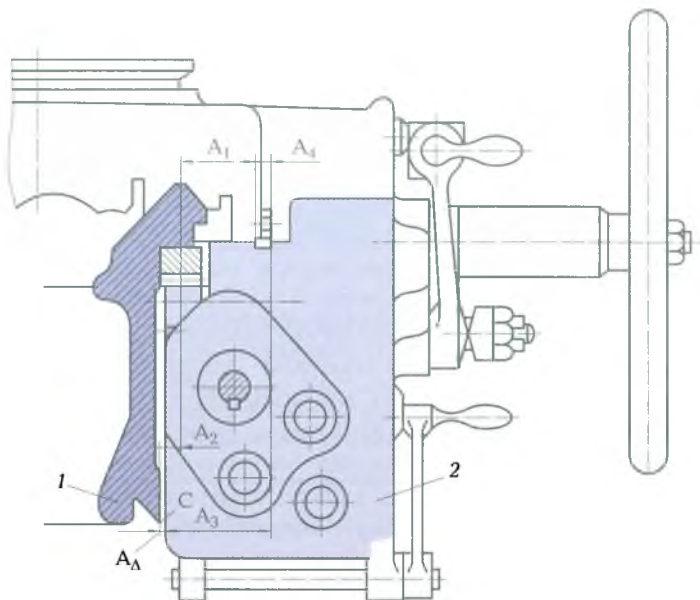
Схема размерной цепи, связывающей необработанную поверхность С фартука с направляющей станины:
